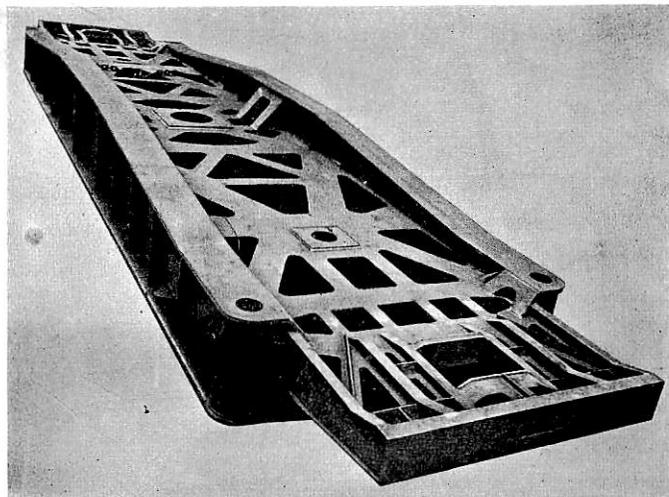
Geschweißte Unterwagenplattform eines Kraftwagens.
